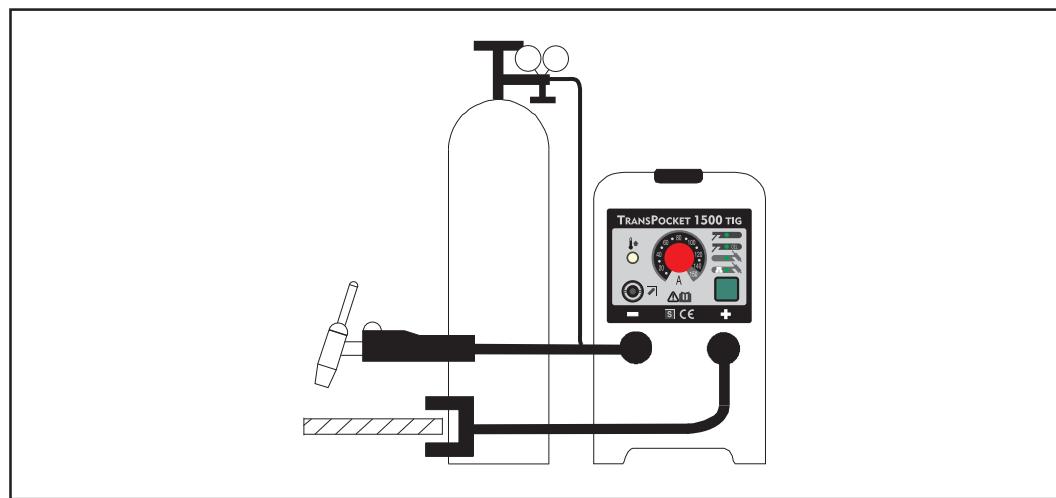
Аппарат TP 1500, приспособленный для сварки TIG.
